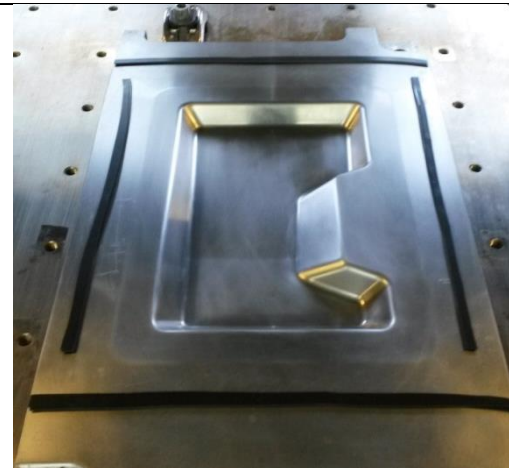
Schikane-WZ, Pressen - Unterwerkzeug
